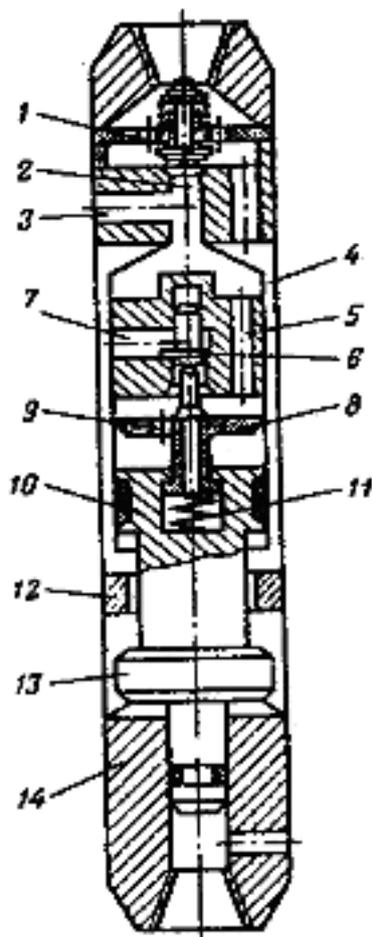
Гидровибратор для ликвидации прихватов: 1 – клапан; 2, 3, 7 – центральный и радиальные каналы; 4 – корпус; 5 – продольный канал; 6, 8 – впускной и выпускной каналы трубореза; 9 – пружина
